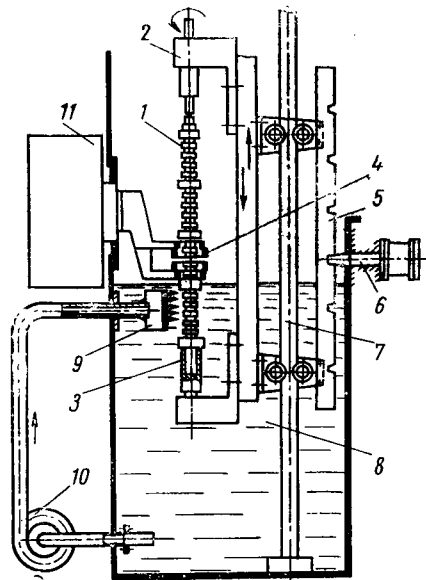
Схема установки для поверхностной закалки кулачков распределительного вала:
